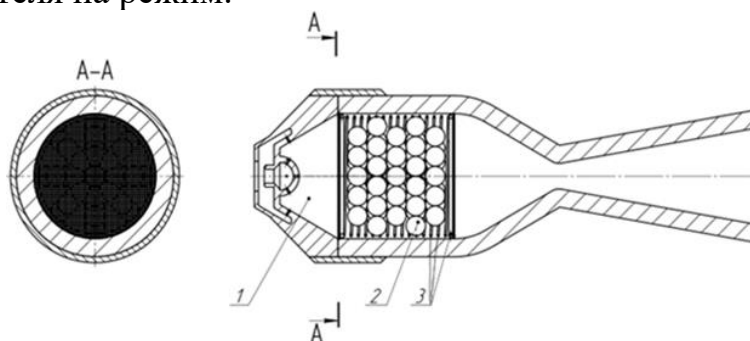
Конструкция камеры ТКРД: 1 – камера двигателя; 2 – каталитический пакет; 3 – нагревательный элемент.
